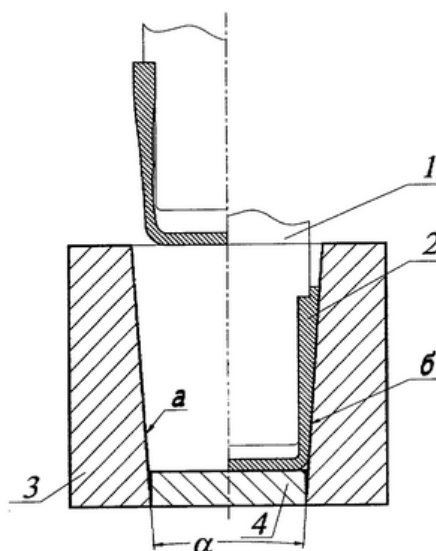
Способ вытяжки изделий из листовых заготовок
